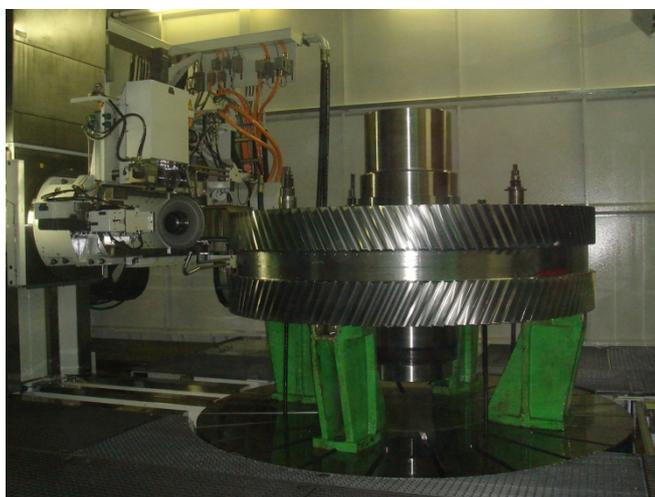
Обработка шевронного колеса червячной твердосплавной фрезой
